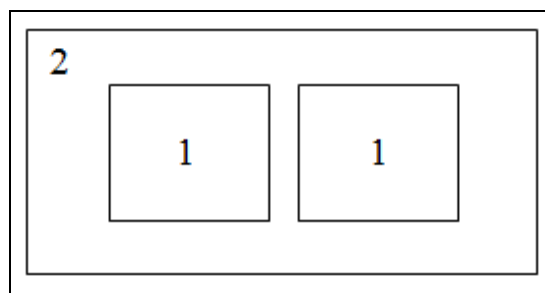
Identification de la zone moulante (1) e de la zone de jointe (2) d'un moule
